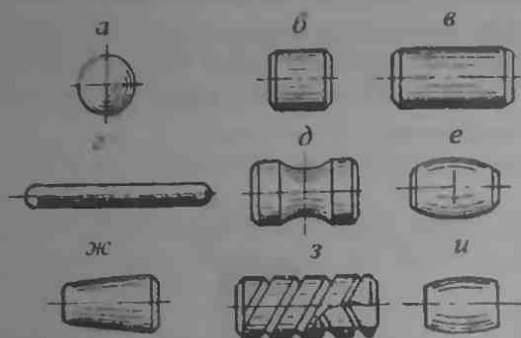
Типы тел качения в подшипниках: а) шарик; б, в) короткий и длинный ролики; г) игольчатый ролик; д) цилиндрический ролик с шейкой; е) бочкообразный ролик; ж) конический ролик; з) витой ролик; и) сферический ролик
